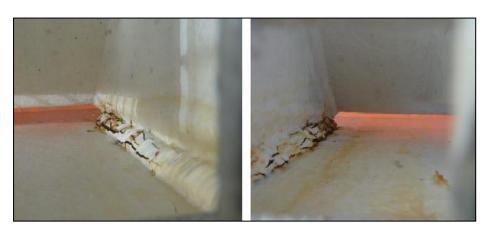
Óxido en las soldaduras de las uniones en la estructura del pescante.
